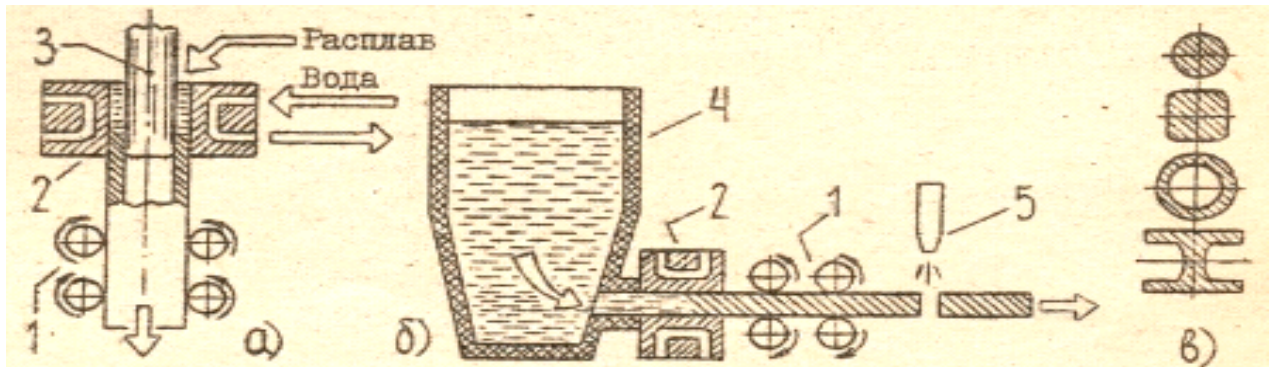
Непрерывное литье: 1 — тянущие валки; 2 — воздухоохлаждаемая изложница; 3 — охлаждаемый стержень; 4 — тигель; 6 — резак
